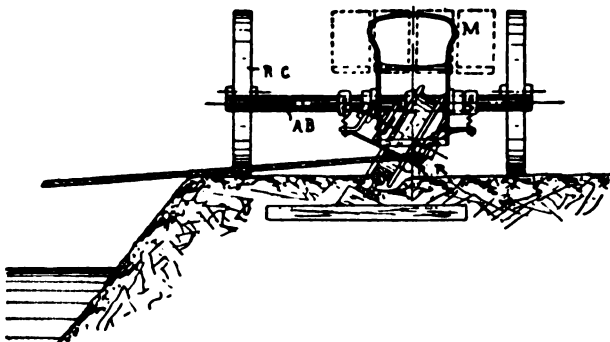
Telaio isopédin per battelli. Prospetto.
